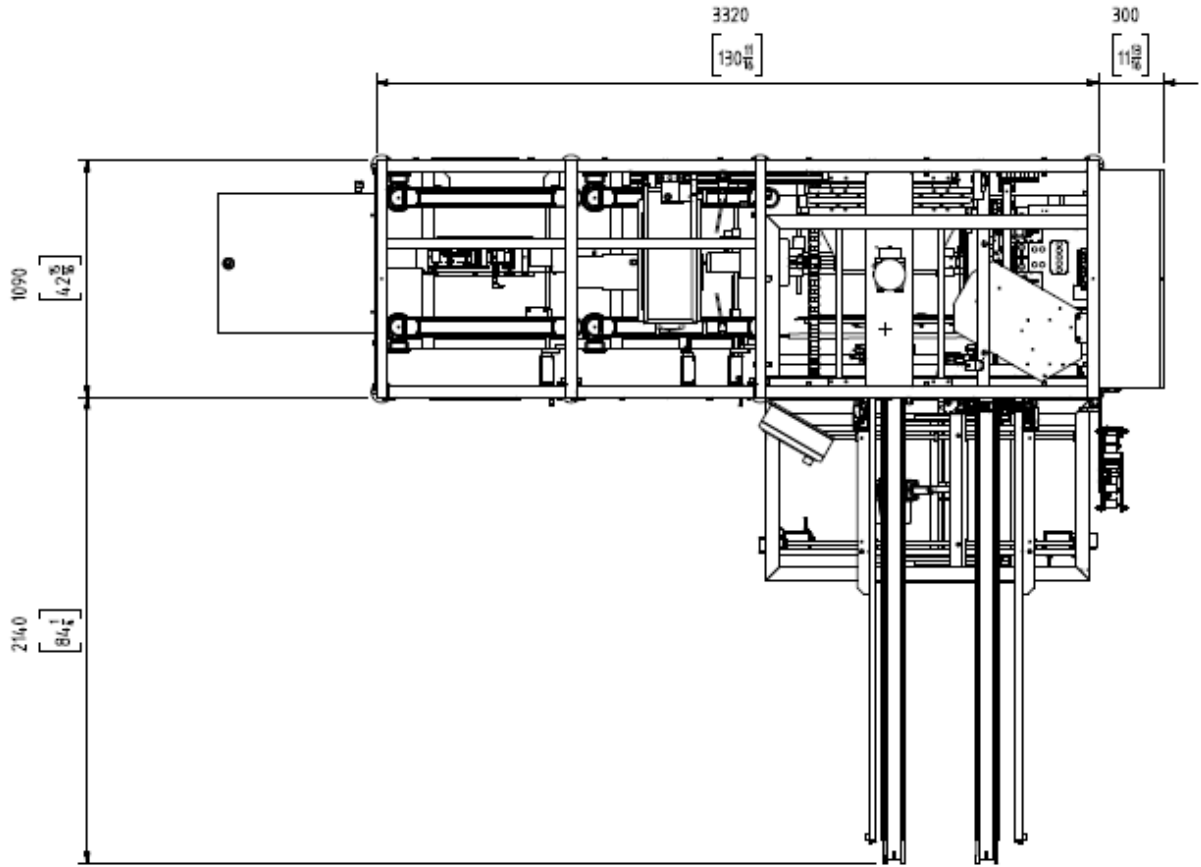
Plano de dimensiones de largo y ancho de armadora LANTECH
